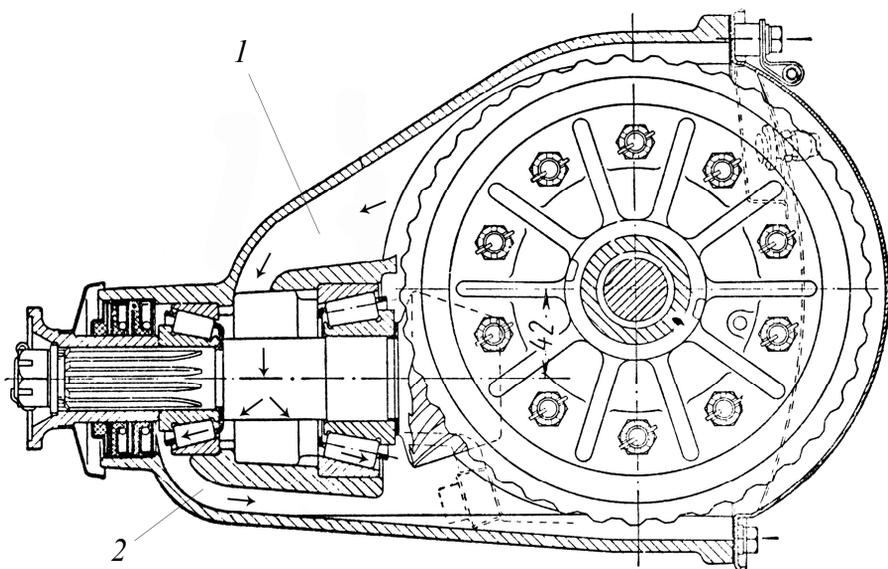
Схема смазки подшипников ведущей шестерни легкового автомобиля
